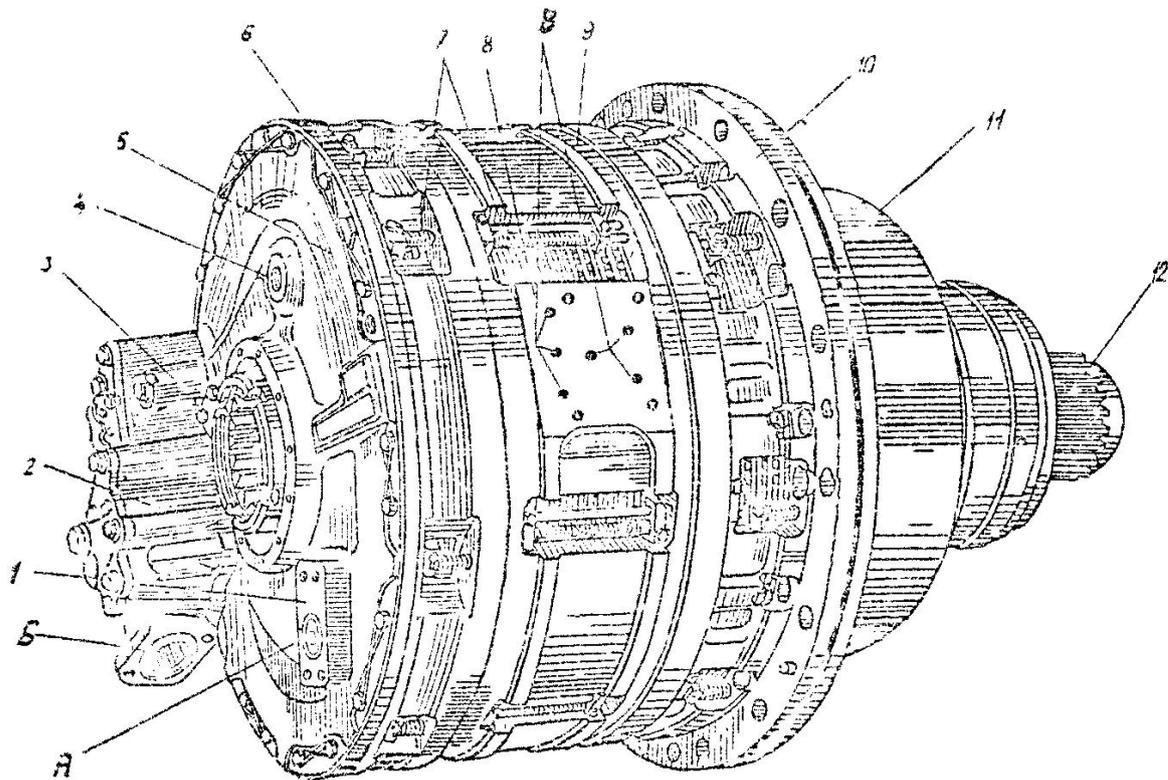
Коробка передач в сборе с бортовой передачей левая:
